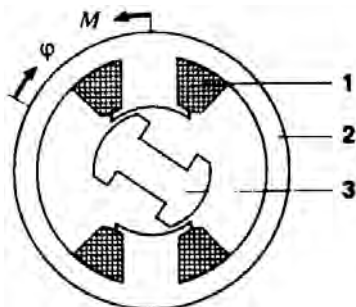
Электромагнитный однообмоточный поворотный исполнительный механизм:
